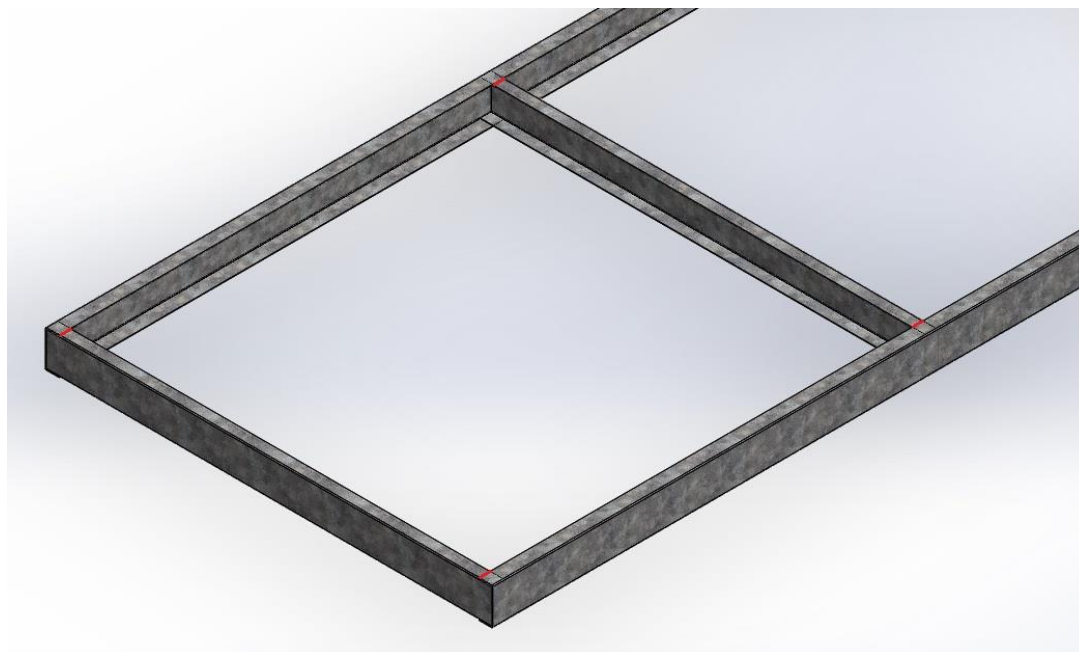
Ilustración de soldaduras en paneles de techo.
